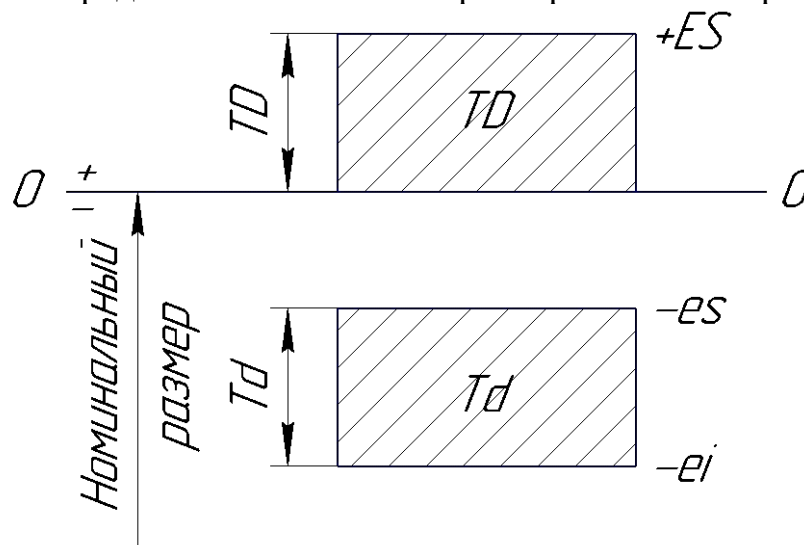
Схемы полей допусков отверстия и вала
